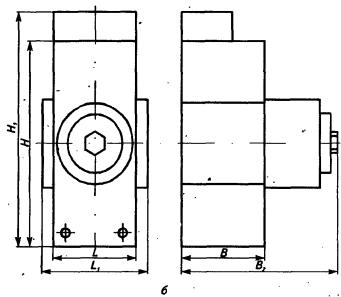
Габаритный чертеж выключателей стационарного исполнения с электромагнитным приводом
